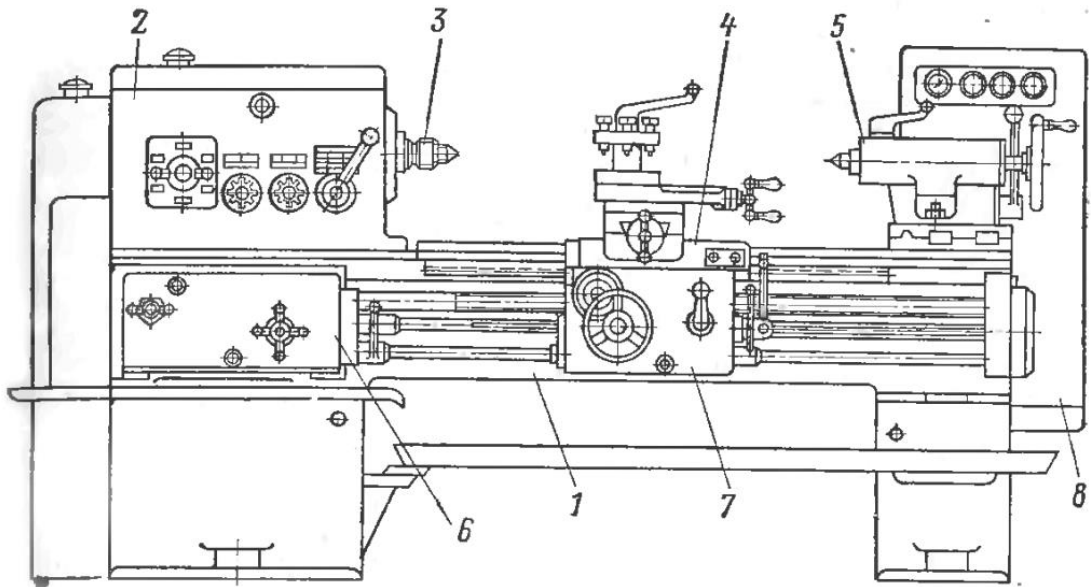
Общий вид токарно-винторезного станка модели 1К62Б
